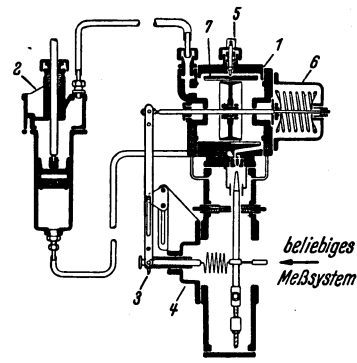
Strahlrohrsteuerwerk mit hydraulischer Rückführung (Askania).
